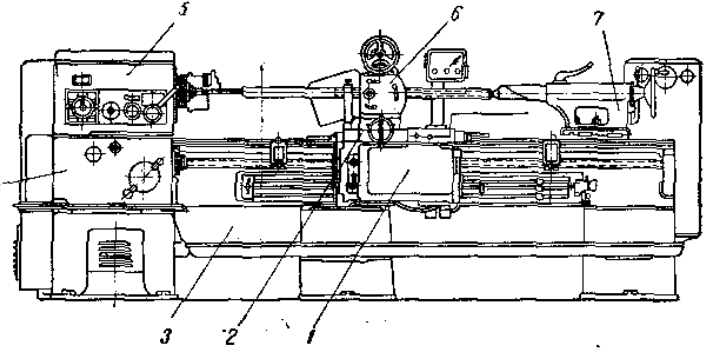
Общий вид резьбофрезерного станка 1К62РВС1:
